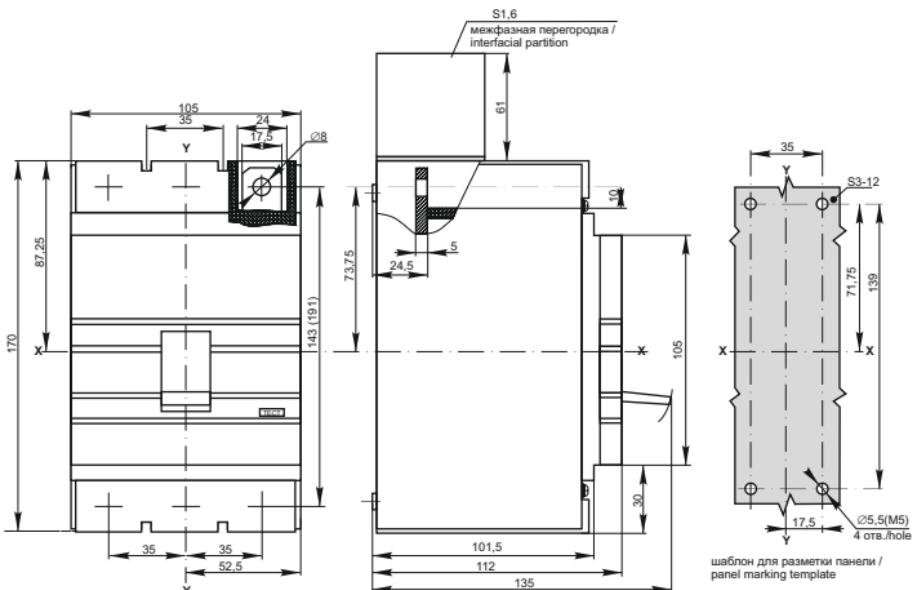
Габаритные и установочные размеры выключателя BA88-35 /
